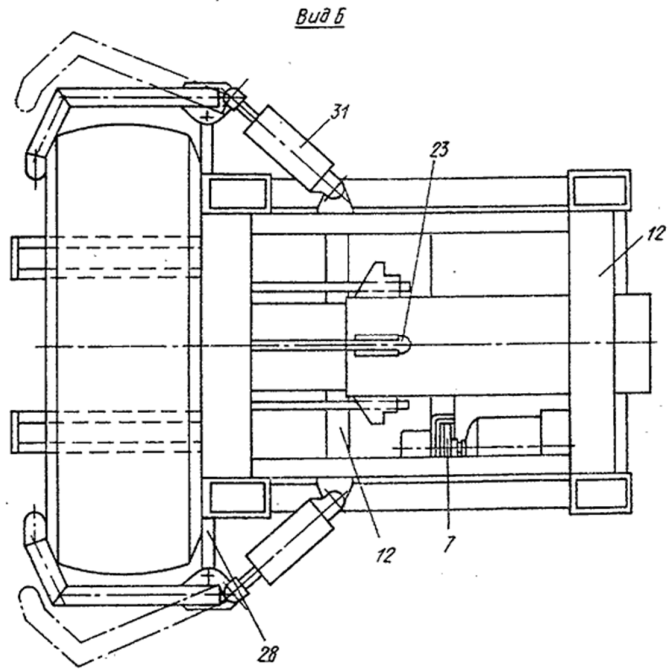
Шиномонтажный стенд, вид Б
